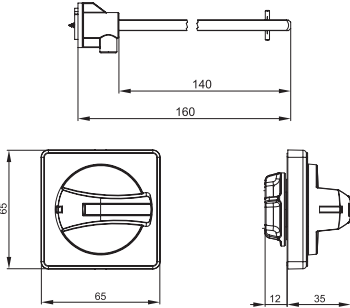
Габаритные и установочные размеры рукоятки выноской / Figure 4 – Overall and mounting dimensions of the extended handle / 4 сурет – Шығармалы тұтқаның габариттік және орнату өлшемдері
